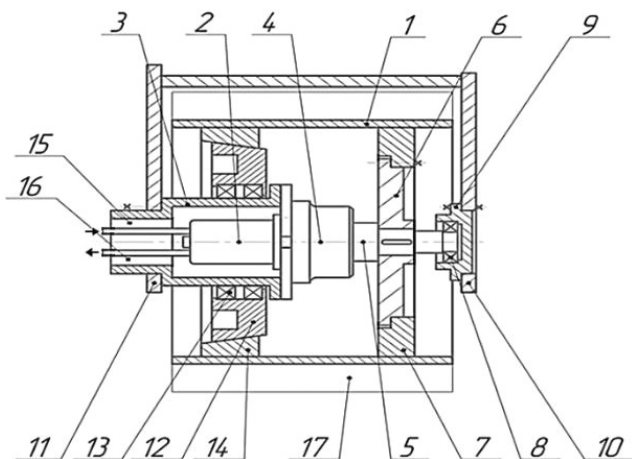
Конструктивна схема фрезерного барабана МХФ
